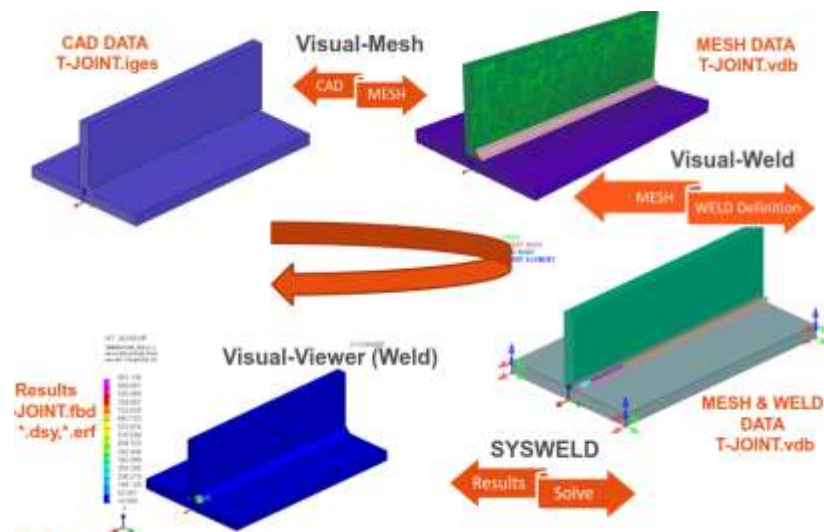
3 Khởi động vào module Welding Advisor và các công cụ chính
